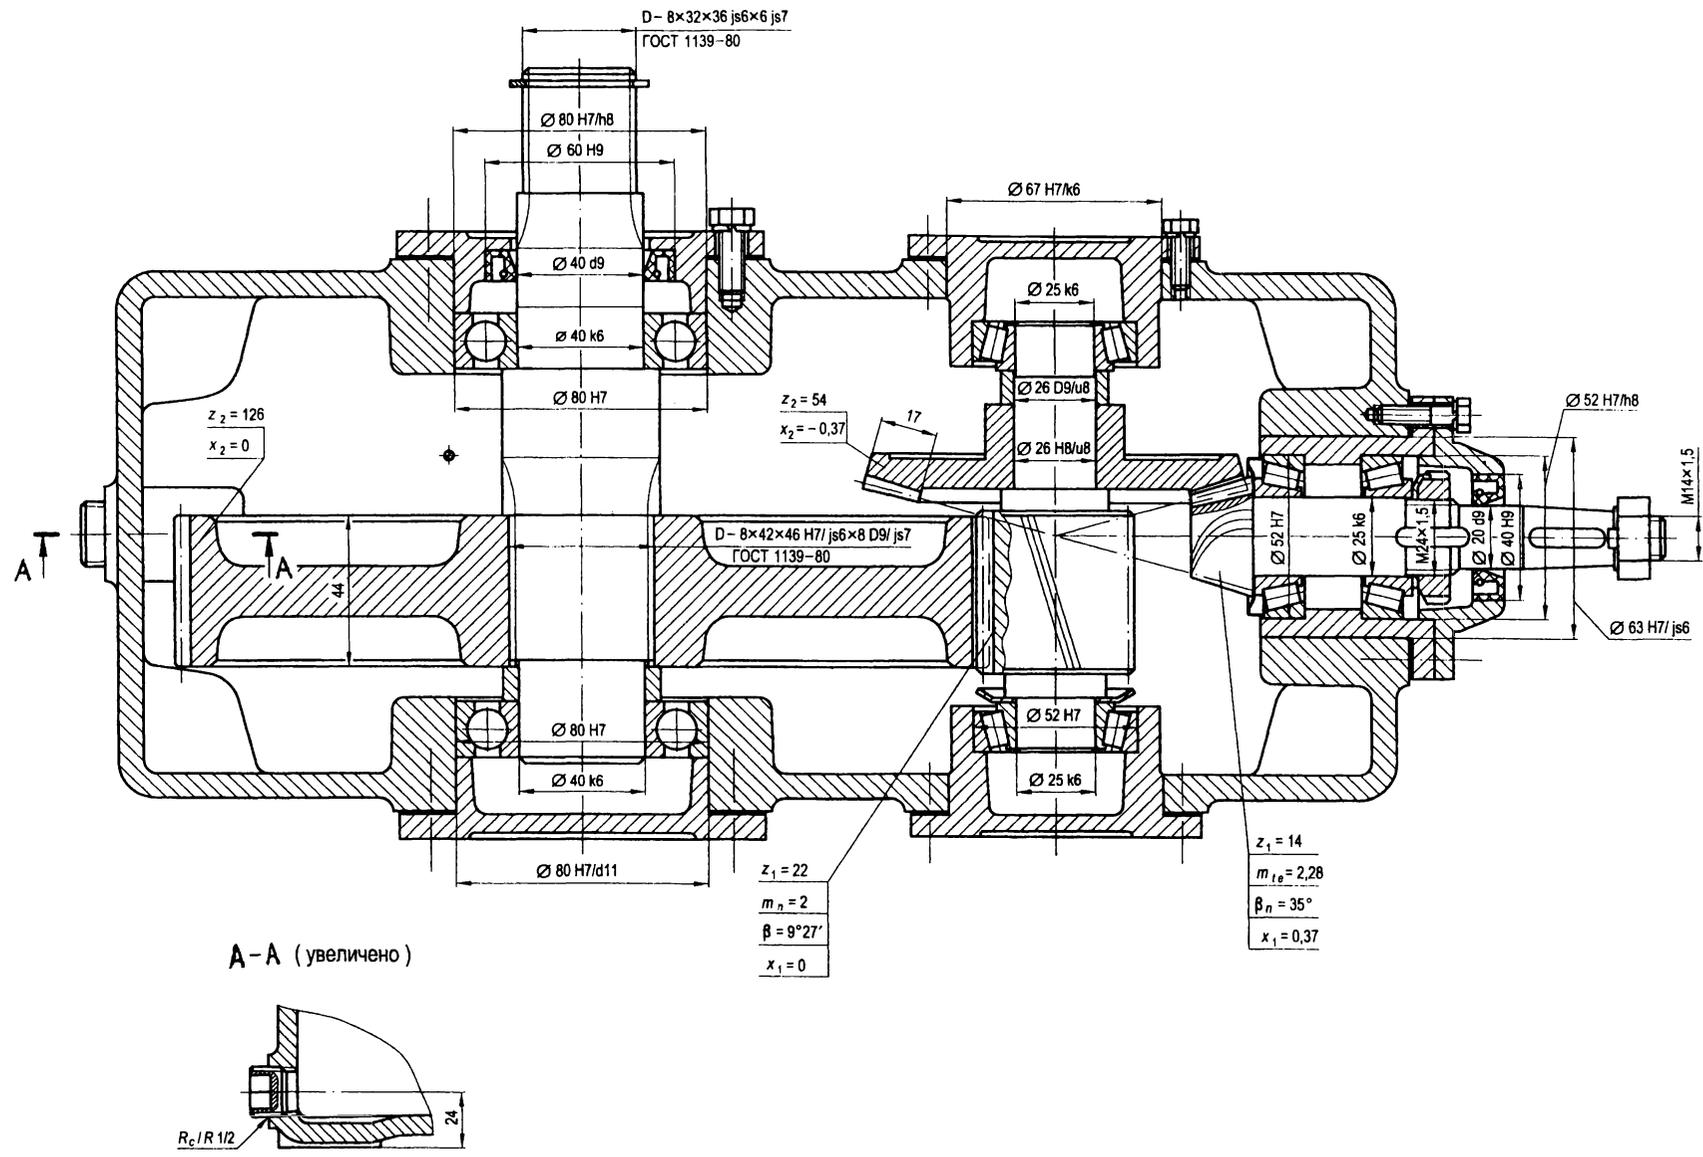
Редуктор коническо – цилиндрический горизонтальный без разъема корпуса по осям валов
